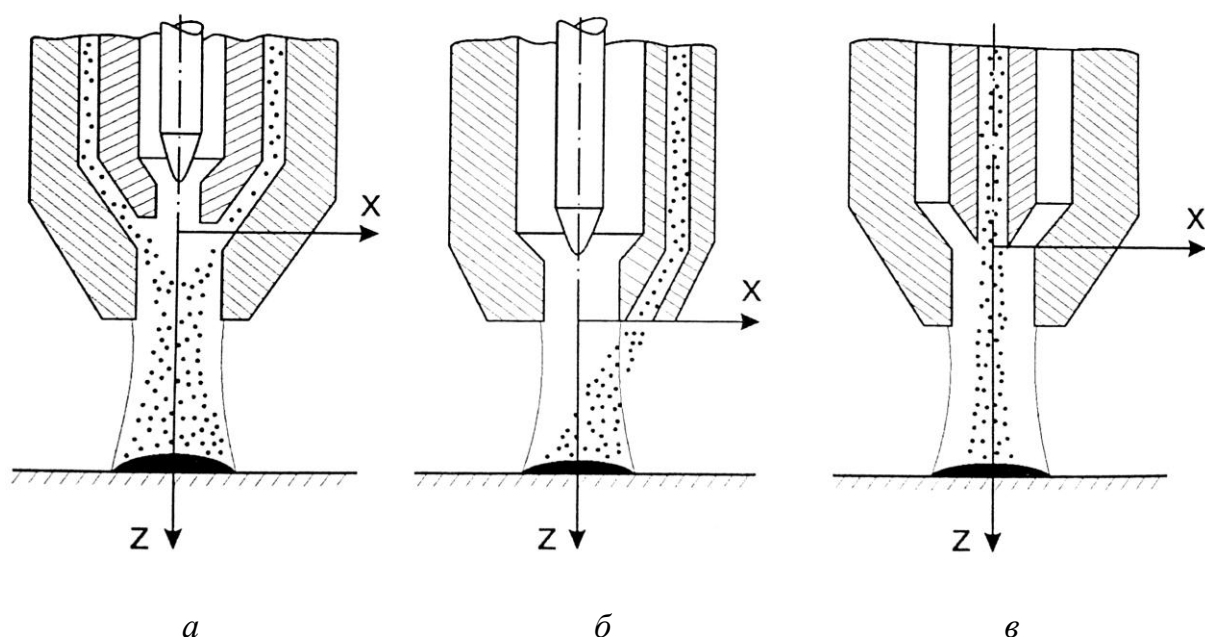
Схемы ввода порошка в дугу при плазменно-порошковой наплавке:
